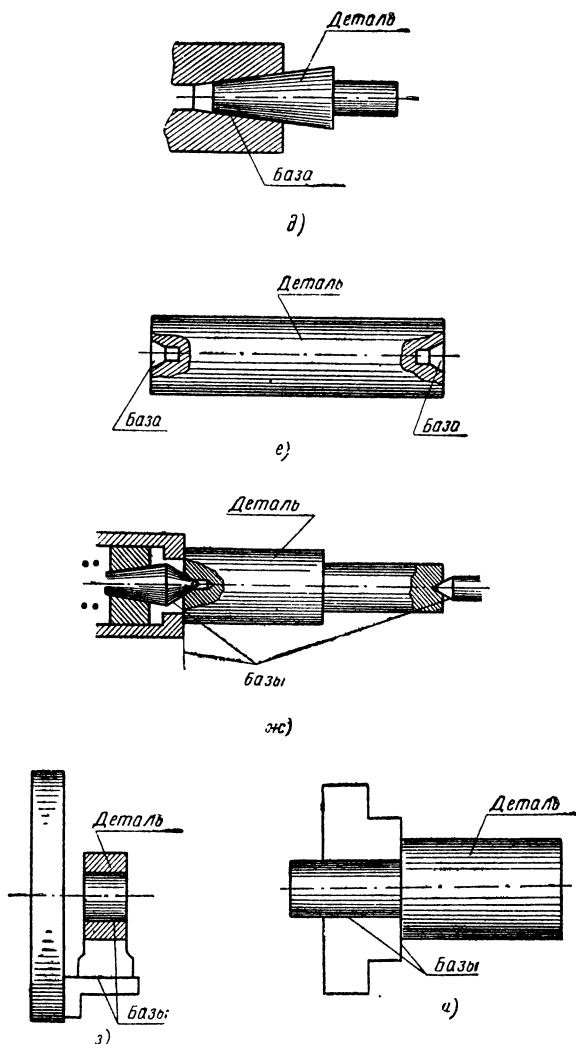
Виды базовых поверхностей при токарной обработке (продолжение):
